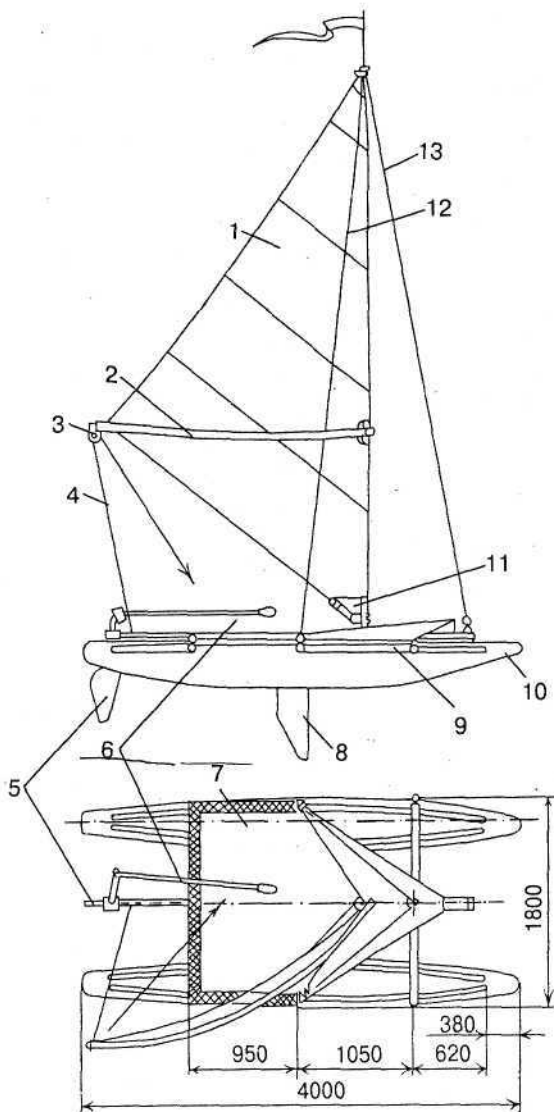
Катамаран «Альтаир» (вид сбоку и сверху): 1 — парус «Стриж»; 2 — гик; 3 — блок шкотов; 4 — гика-шкоты; 5 — перо руля; 6 — удлинитель румпеля; 7 — палуба; 8 — шверт; 9 — козырек-брызгоотбойник; 10 — поплавок; 11 — мачта; 12 — ванта; 13 — штаг
